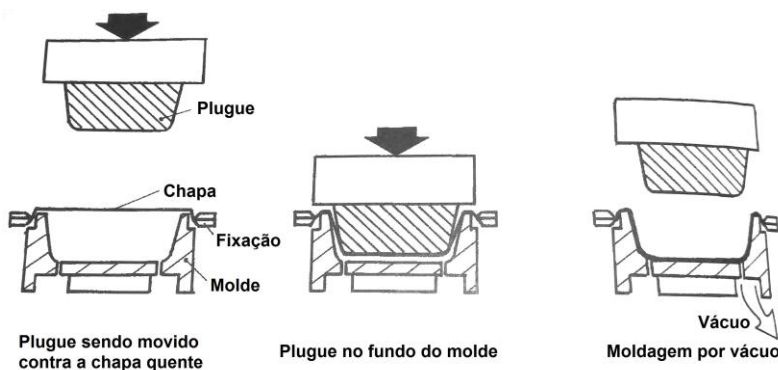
Pré-moldagem com plugue seguida de moldagem por vácuo.
